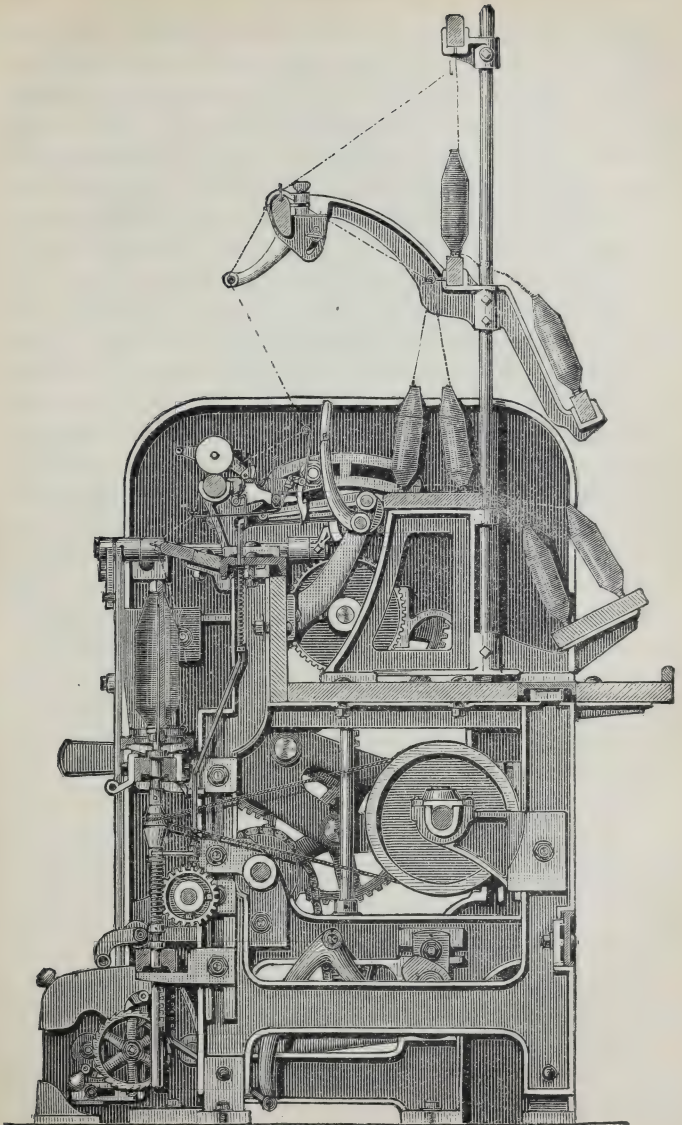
Ringzwirnmachine der Sächf. Maschinenfabrik.
